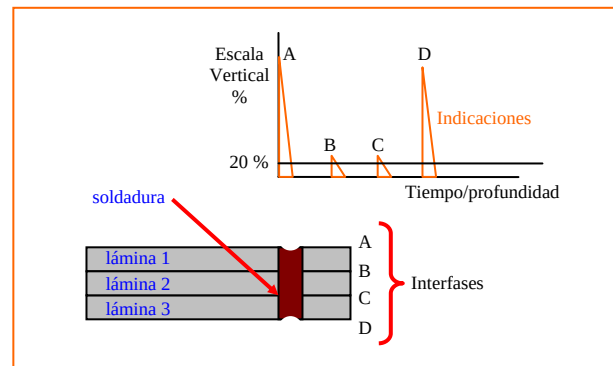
Indicaciones en la evaluación de soldaduras láser
